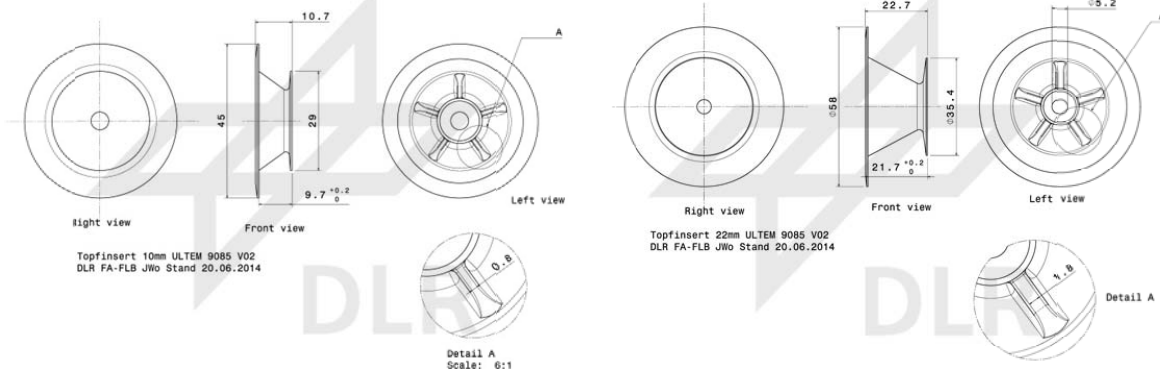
Dimensionsmaße des Insertprototyps Topfinserter ULTEM 9085, 10 mm (für Sandwichtyp 616 HC).
